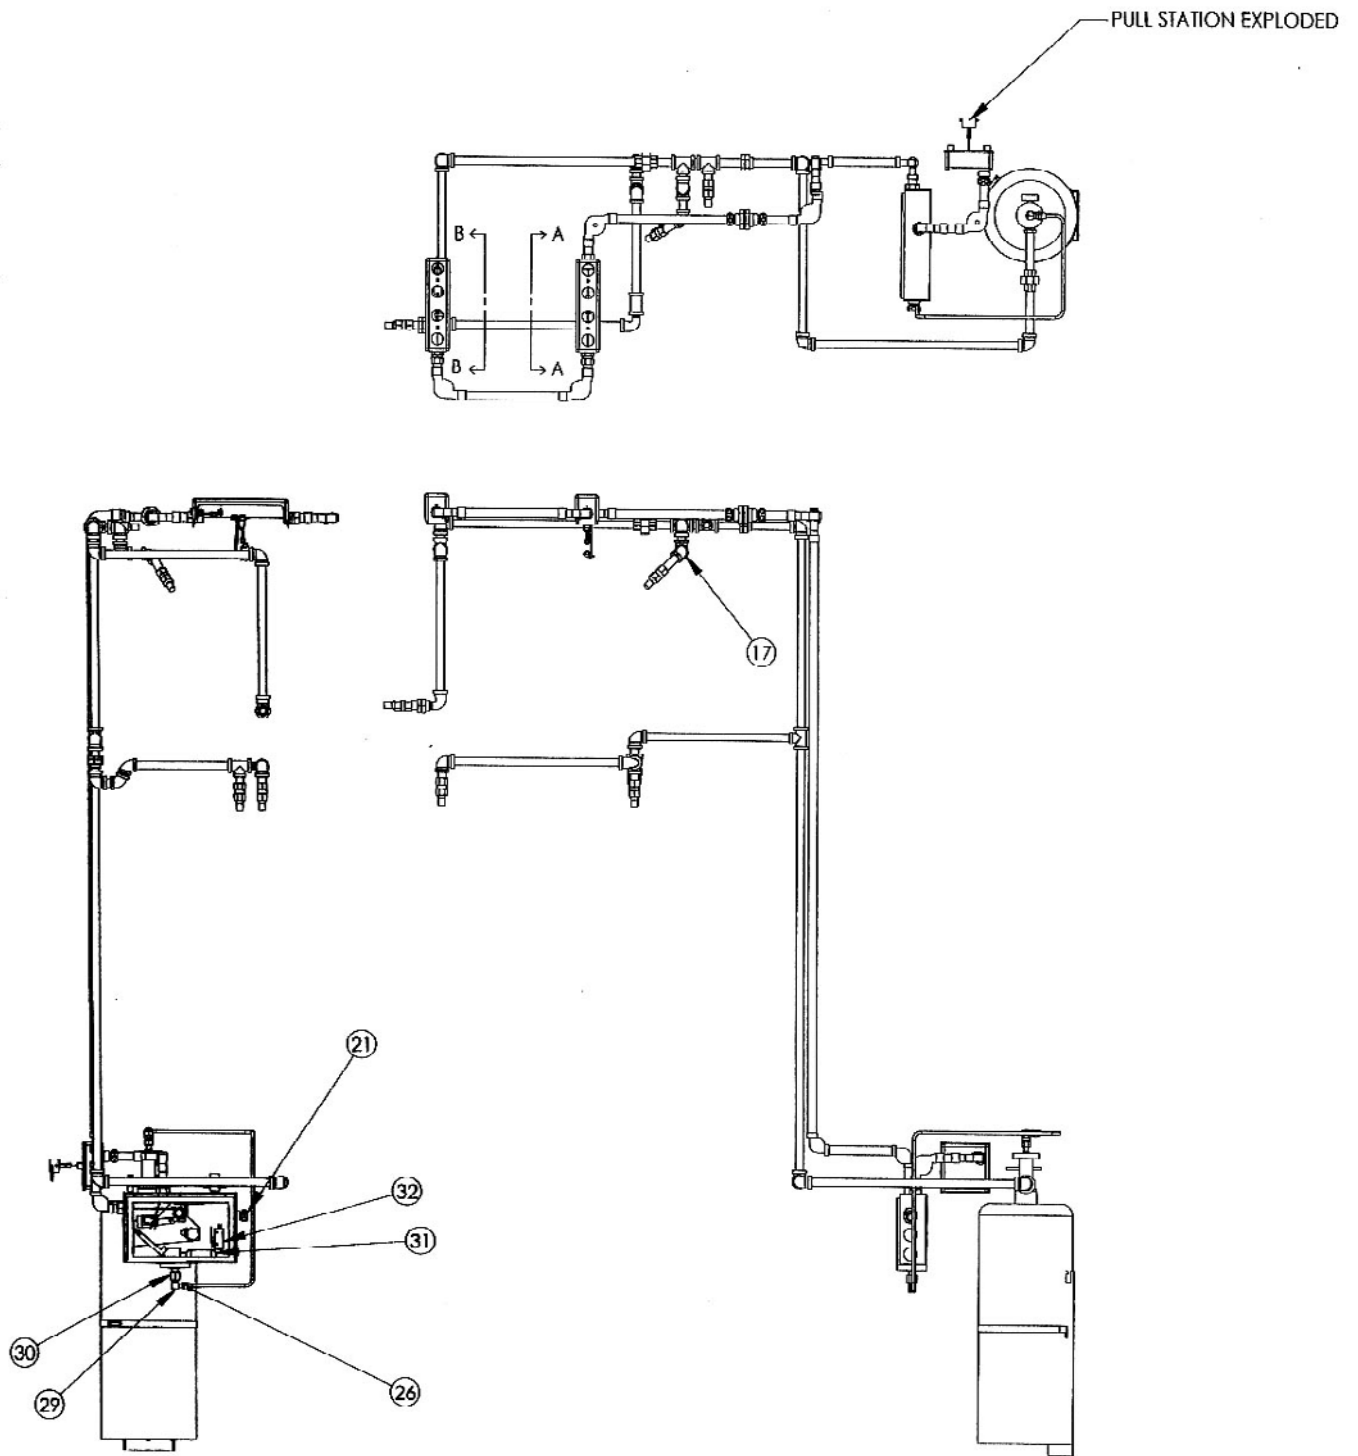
ENSAMBLAJE DEL SISTEMA EXTINTOR DE FUEGO DEL INSIDER.
